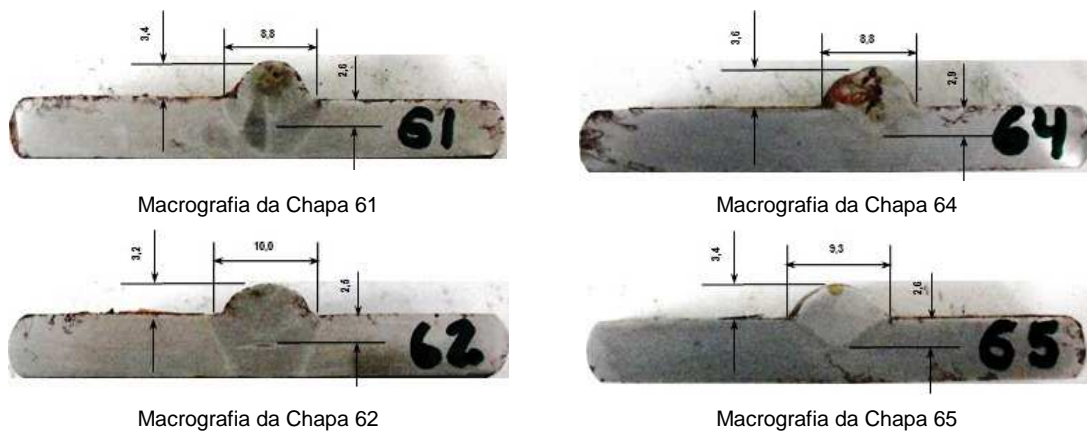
Macrografias com altura do reforço (r), largura do cordão de solda (b) e a penetração das soldas com Ar+6% H_2 .
